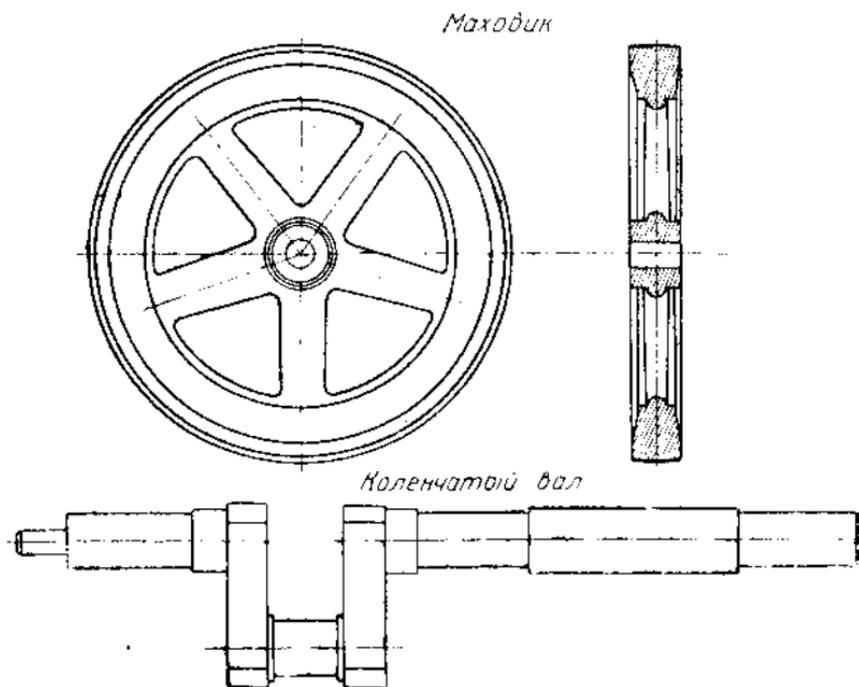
Главный (коленчатый) вал и маховик рамной пилы
